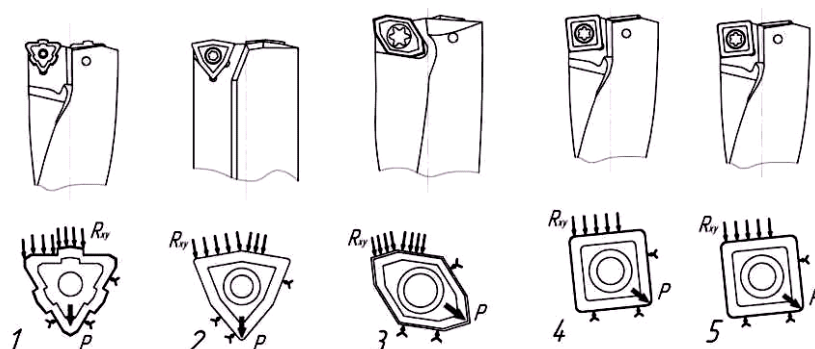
Схемы базирования и крепления периферийной режущей пластины сборного сверла фирмы:
